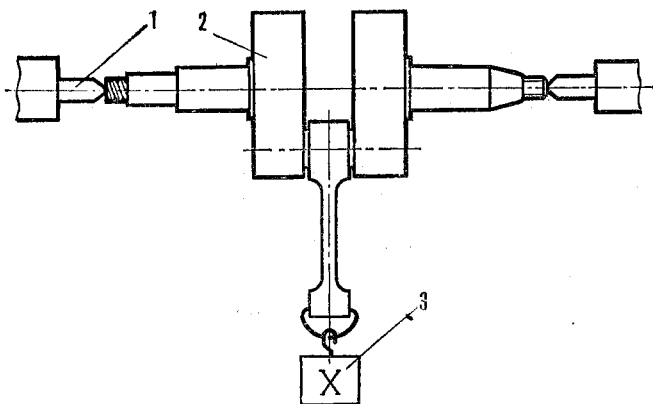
Схема уравнивания коленчатого вала: 1 — вращающийся центр; 2 — коленчатый вал; 3 — балансировочный груз
